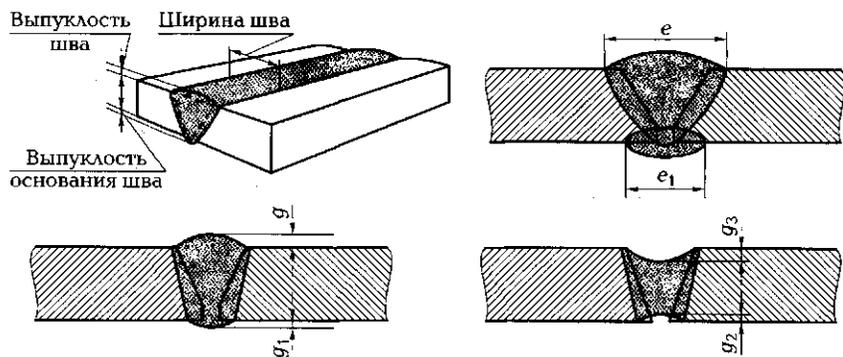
Конструктивные элементы стыкового сварного шва:
